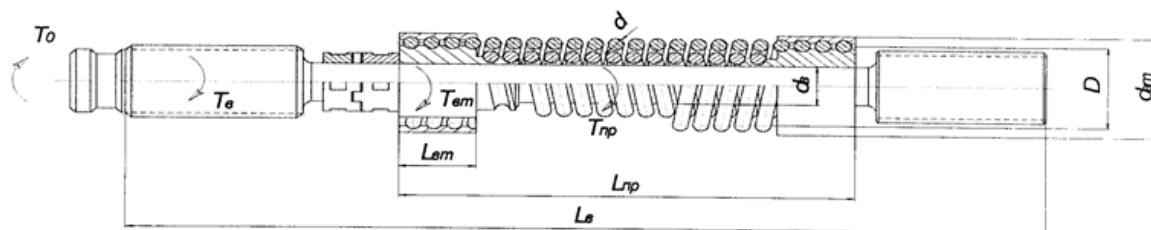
Розрахункова схема ЗЗЖ нової конструкції
